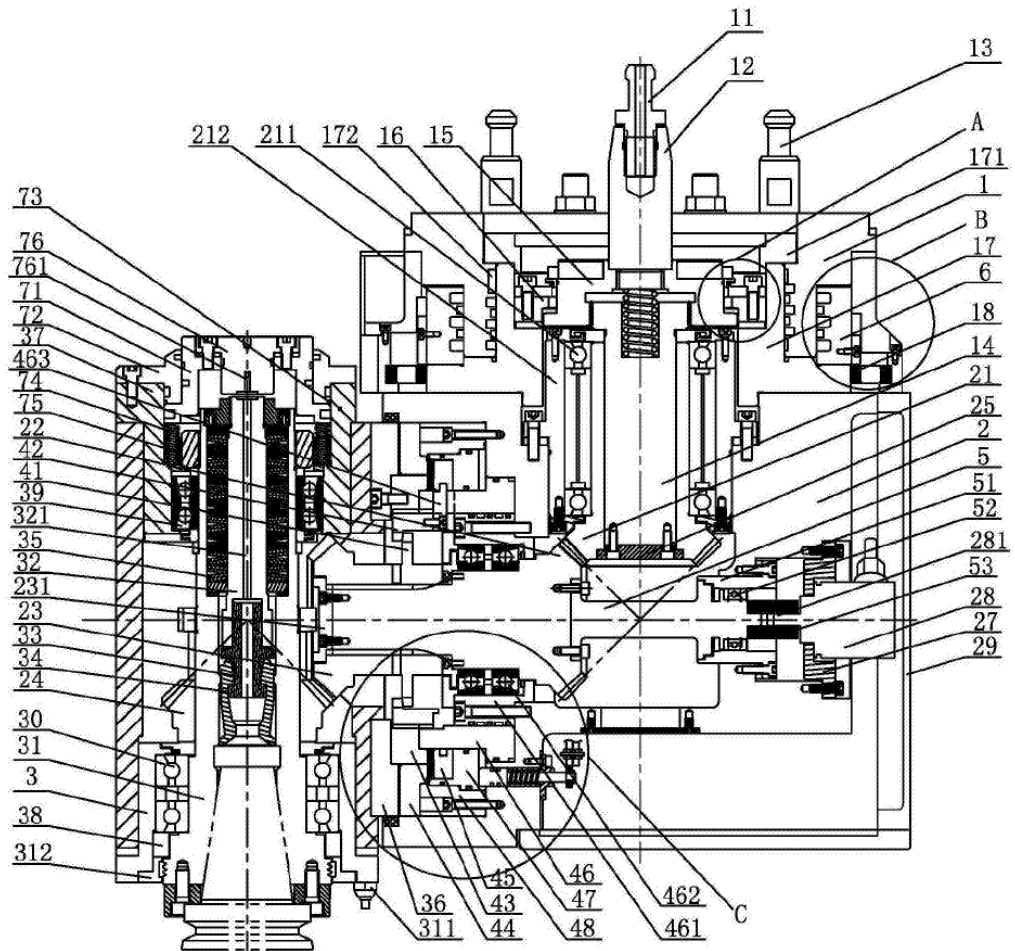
Automatická frézovací pravoúhla hlava IFVW 101 od firmy škoda [8]
